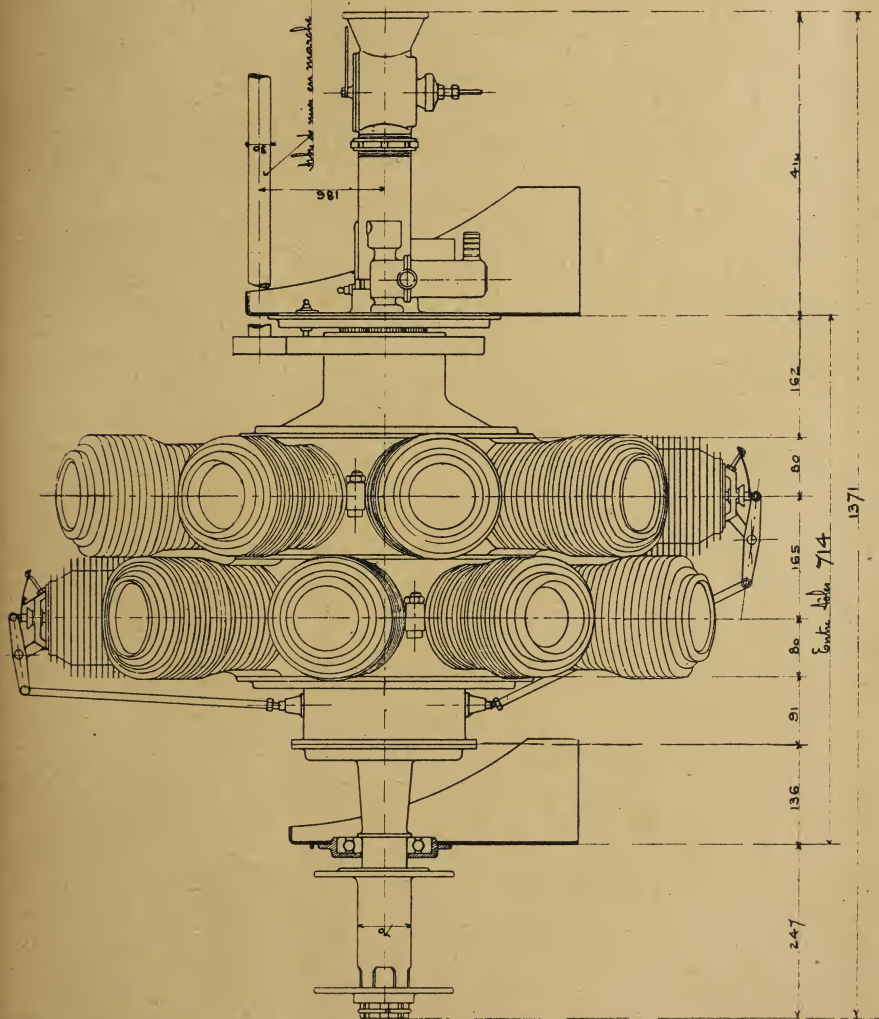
Derselbe Motor wie Fig. 179. Ansicht von der Seite.
